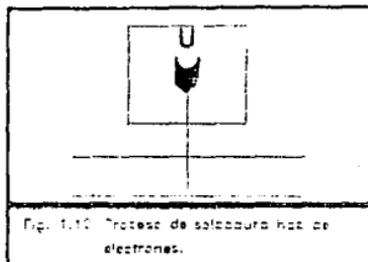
Proceso de soldadura por haz de electrones.
